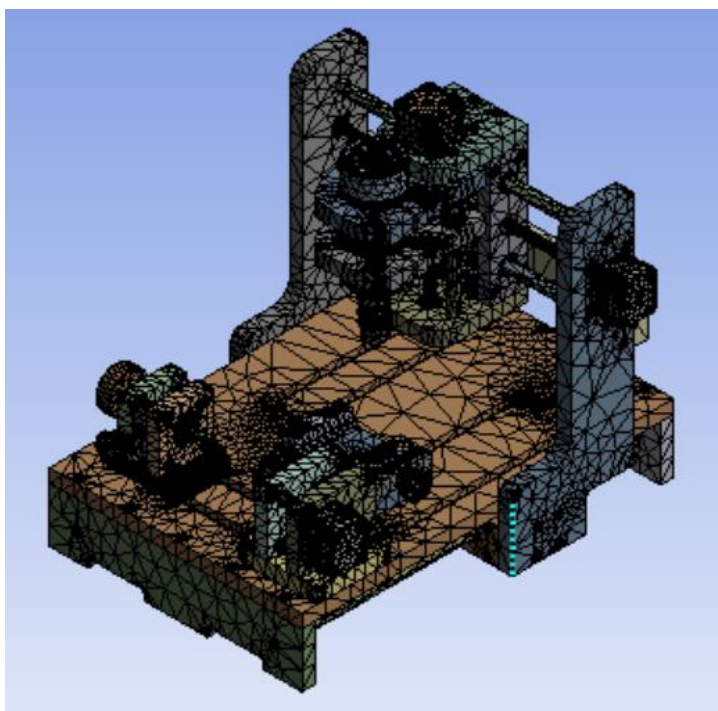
Типова сітка для вертикально-фрезерного верстата
